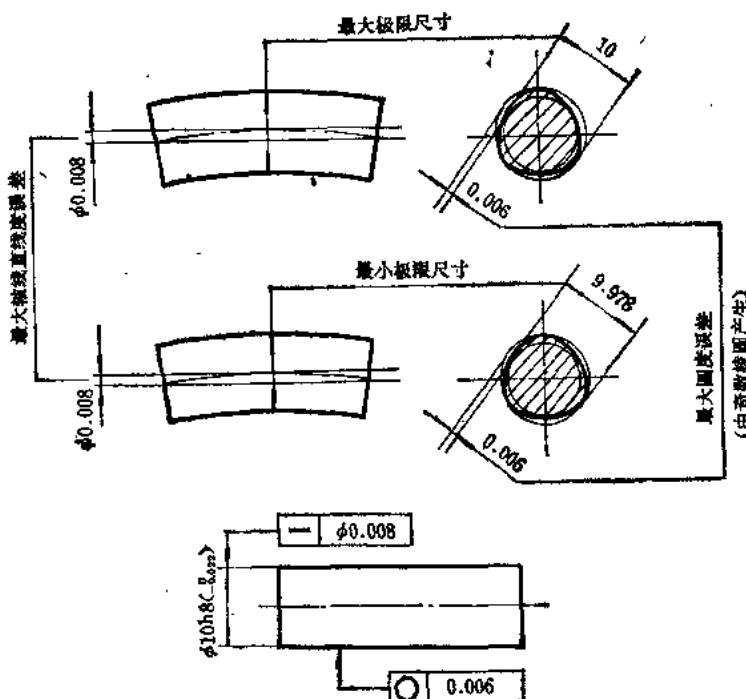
采用独立原则的销轴其形状公差与尺寸公差无关
